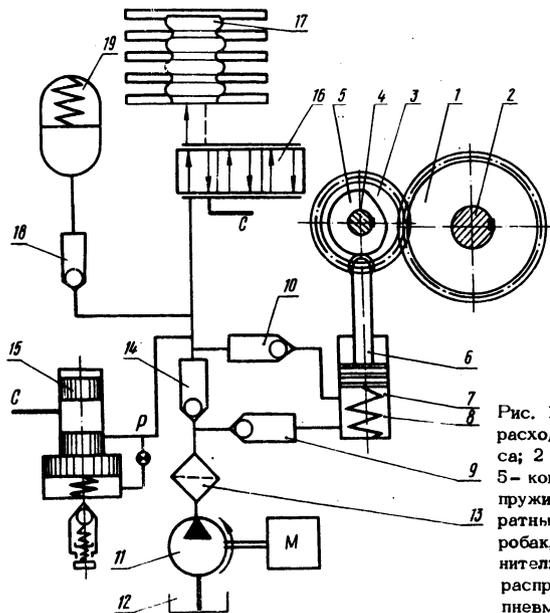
Схема устройства изменения расхода жидкости: 1,3 — зубчатые колеса; 2 — вал основного ротора; 4 — вал; 5 — копир (кулачок); 6 — поршень; 7 — пружина; 8 — цилиндр; 9,10,14,18 — обратные клапаны; 11 — насос; 12 — гидробак; 13 — фильтр; 15 — предохранительный клапан; 16 — плоский гидрораспределитель; 17 — трубка-заготовка; 19 — пневмоаккумулятор.
